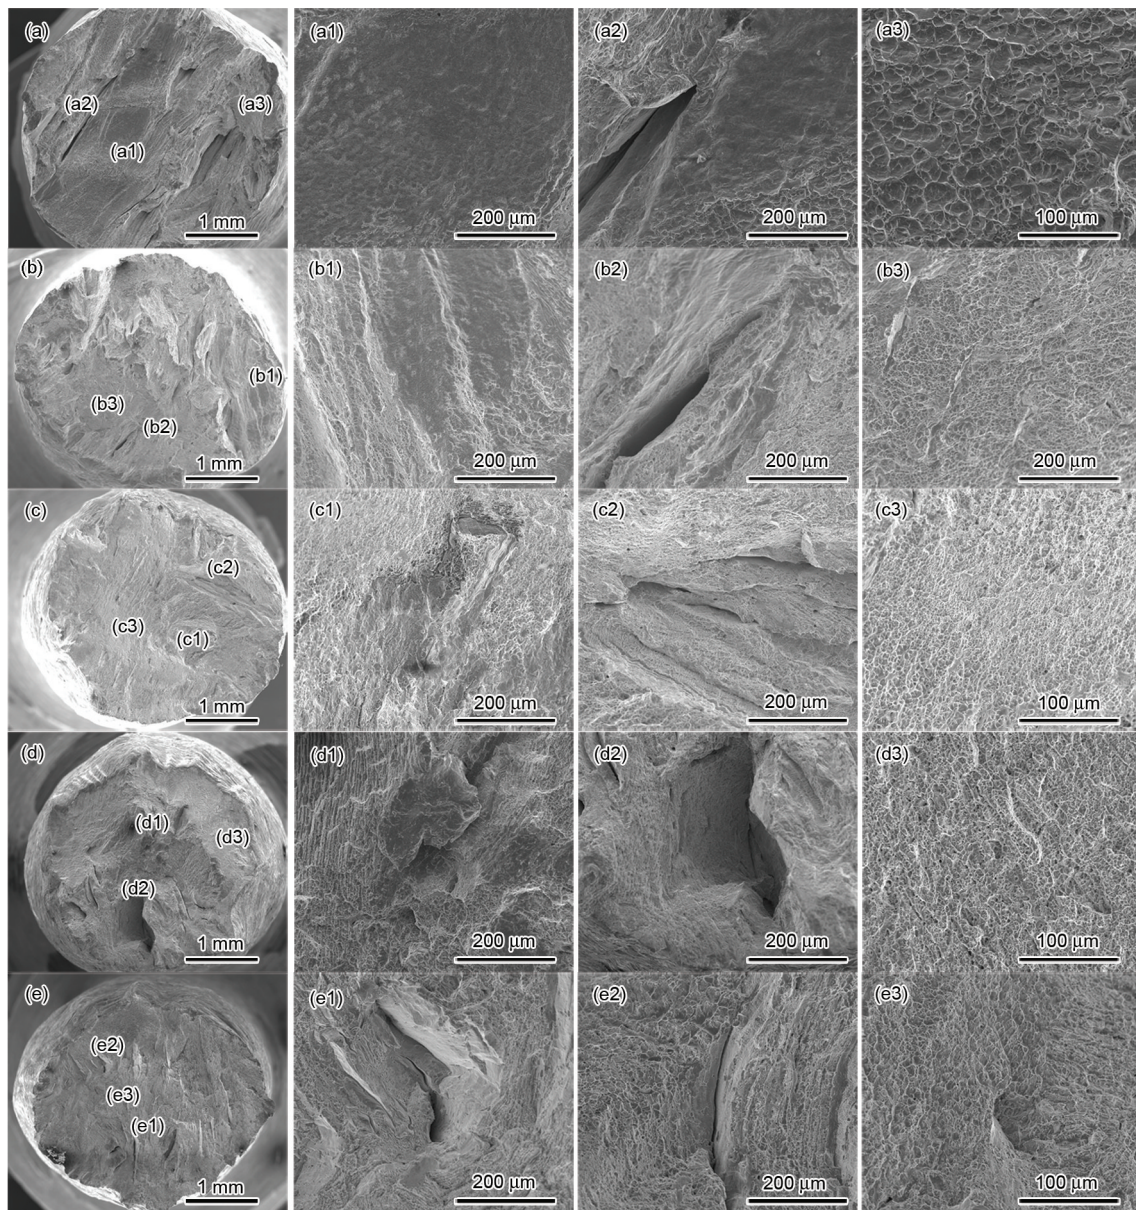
不同 Nb 含量焊缝金属室温拉伸断口形貌
